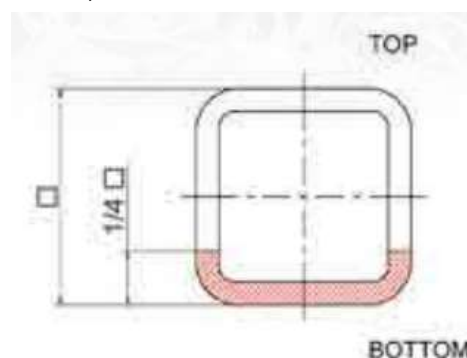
Zones on la soldadura no està permesa (ADR systems)
